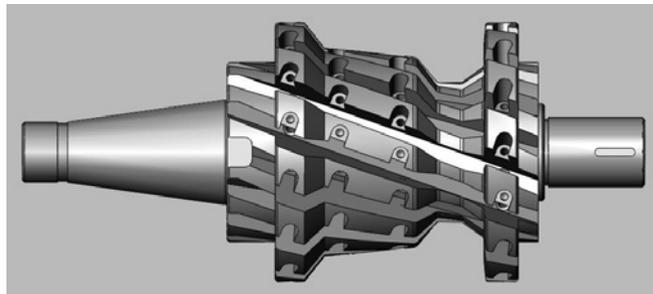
Модель корпуса фрезы с пазами под ножи и пазами под клинья
